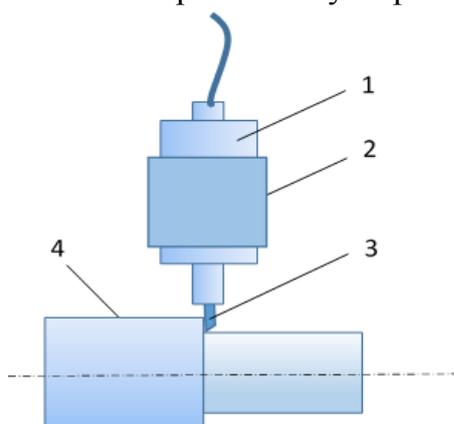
Схема установки для токарной обработки образца совместным воздействием механического резания и ультразвуковых колебаний
